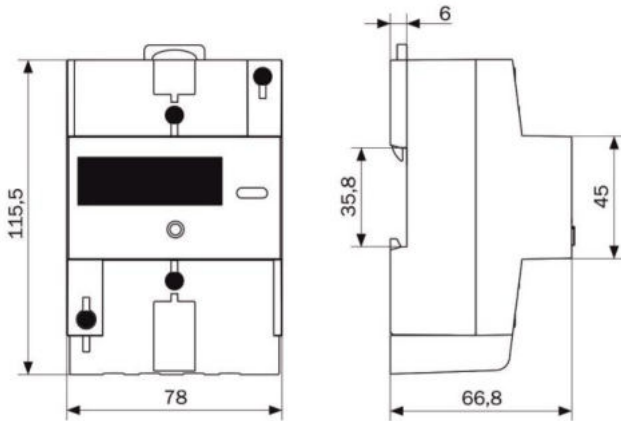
Внешний вид и присоединительные размеры счетчика однофазного ТОГАЗ 103
